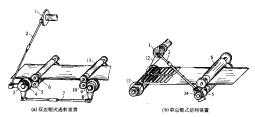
卧键送科装置结构示意图 1- 備心哉; 2-拉杆; 3、8-超結內益; 4、5、9、10-齿轮; 6、11-提轮; 7-掺杆; 12-皮带; 13-苍箭; 14-排轮
